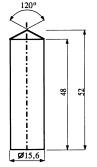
Цилиндрический бронзовый поршень; размеры в мм
